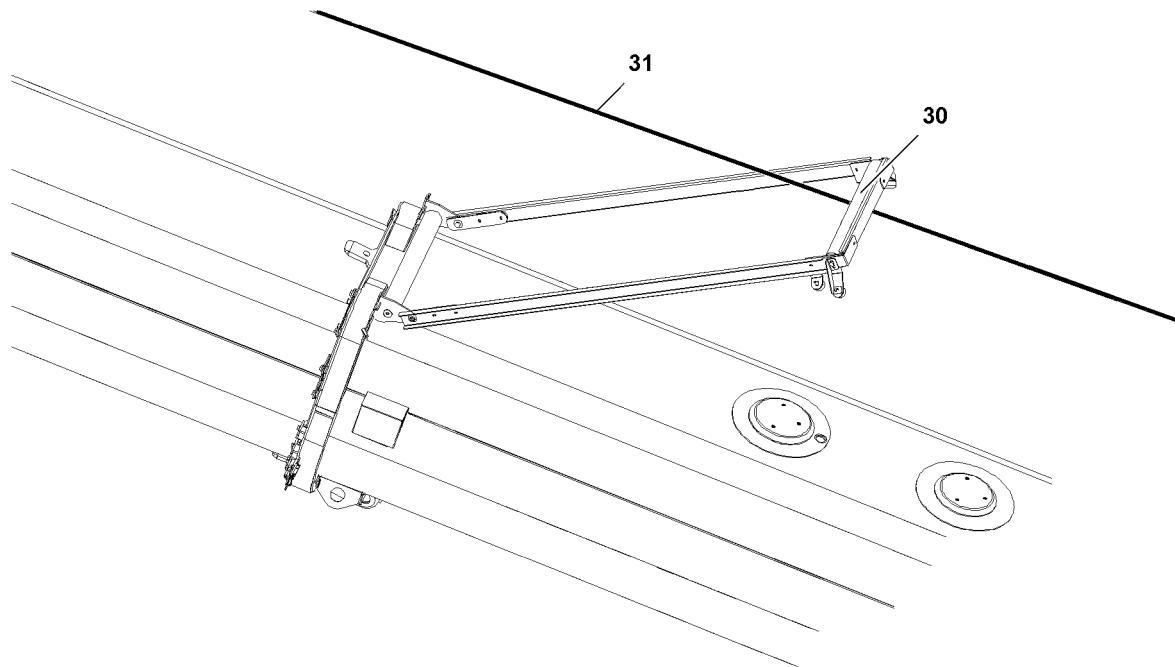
Recorrido del cable de elevación debajo del estribo del cable de elevación 30
